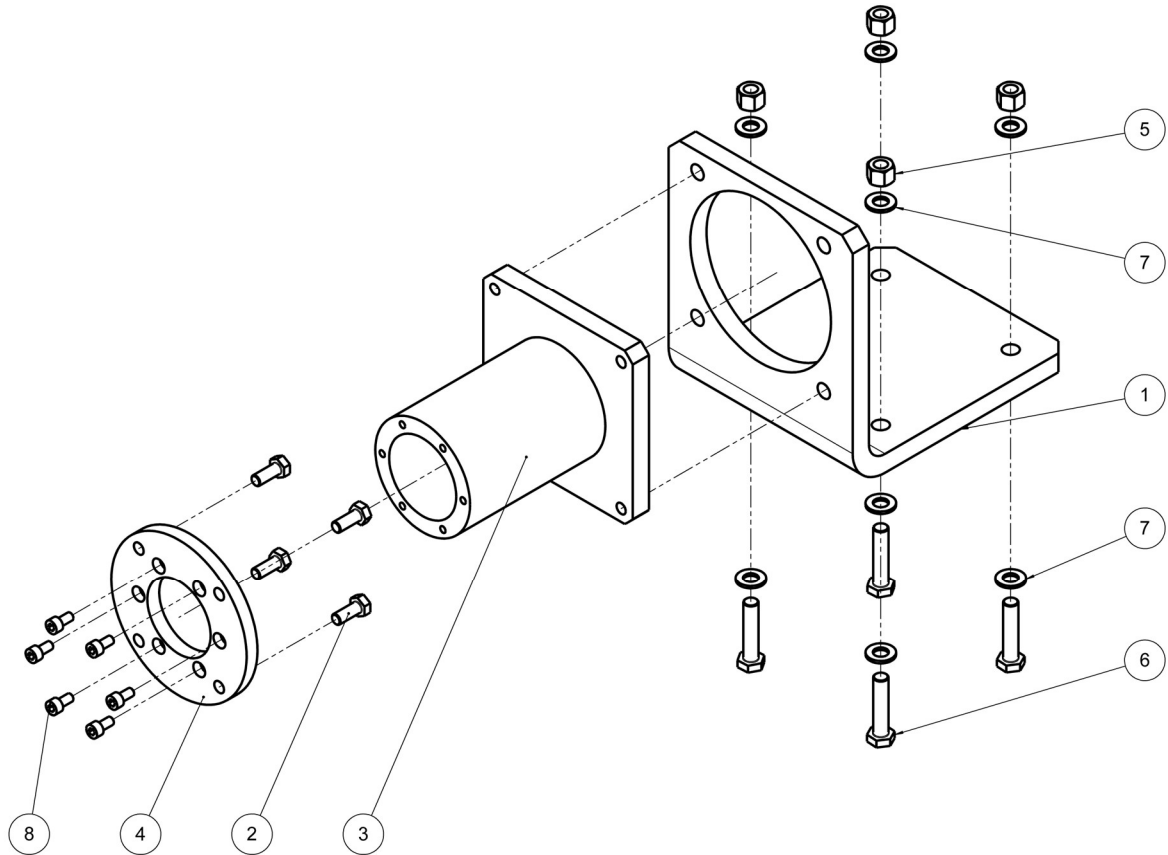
Baugruppe Motorflansch PQ5T-HT
